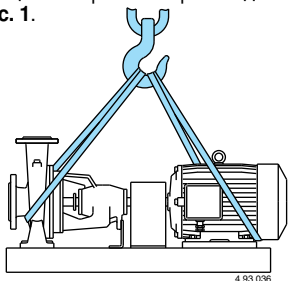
Строповка канатами для поднятия двигатель-насосного агрегата.
